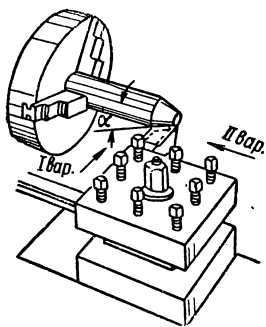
Схема обтачивания конической поверхности широким резцом.
